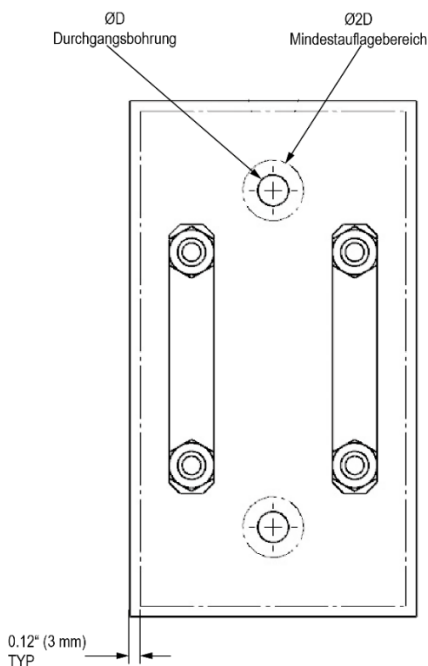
Unterseite des Basis-Ladekontakts mit Darstellung der Montagebohrungen und dem Mindestauflagebereich
